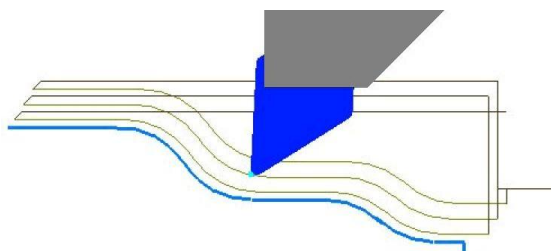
Hrubovací a pravouhlé soustružení [32]
